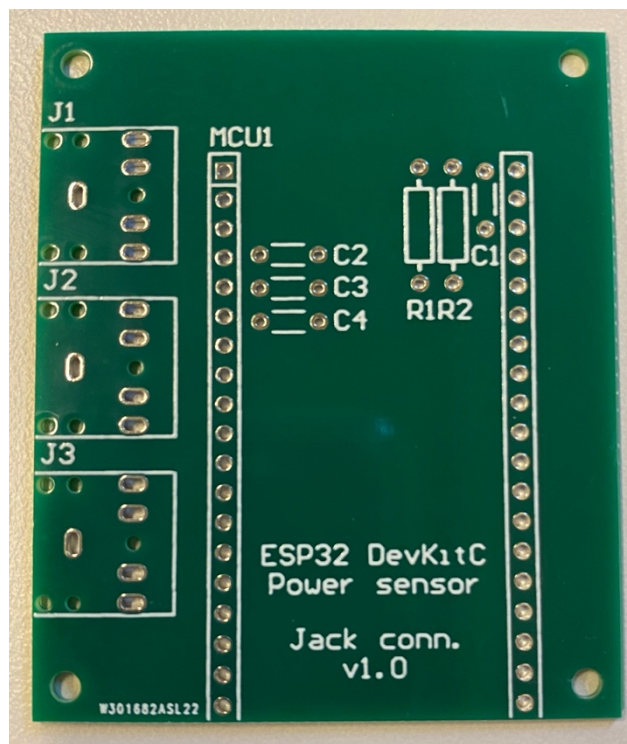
PCB (Printed Circuit Board) amb coure d'una sola capa que s'ha utilitzat.
